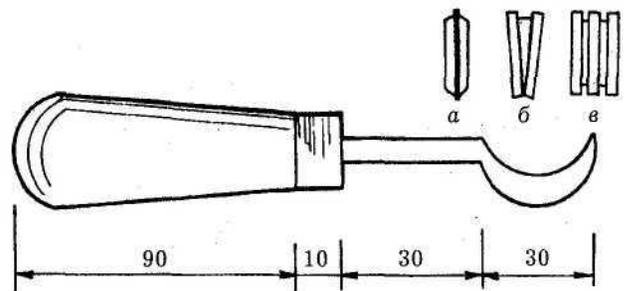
Резцы: а — одинарный; б — двойной; в — тройной
